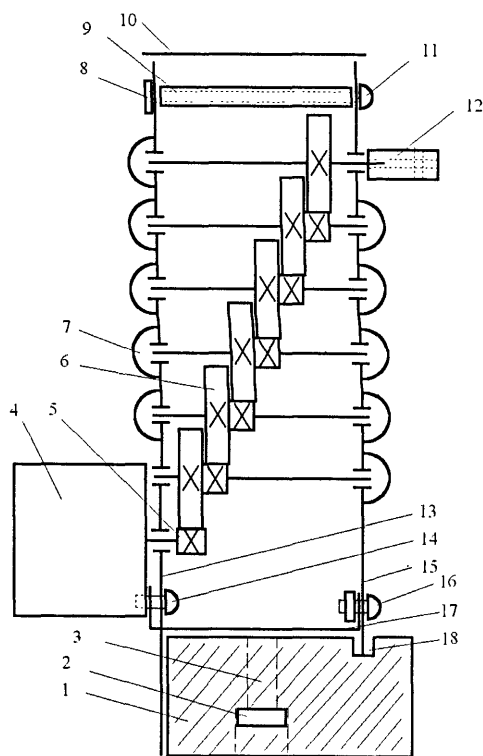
Редуктор: 1 — рейка крепления редуктора; 2 — гайка; 3 — отверстие  $\varnothing 6$  мм; 4 — двигатель редуктора; 5 — шестерня вала двигателя; 6 — шестерни редуктора; 7 — эпоксидные упоры валов шестерен; 8 — гайка стяжного винта; 9 — втулка стяжного винта; 10 — прижимная крышка; 11 — стяжной винт; 12 — втулка выходного вала; 13, 15 — корпус редуктора; 14 — винт крепления к корпусу двигателя и скобы; 16 — винт крепления скобы к корпусу; 17 — скоба; 18 — паз
